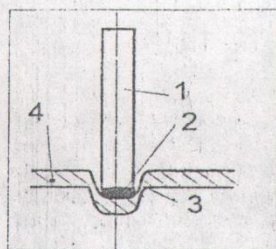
Поперечное сечение сварного соединения: 1-стержень, 2-зона расплавления, 3-зона утонения, 4-труба.
